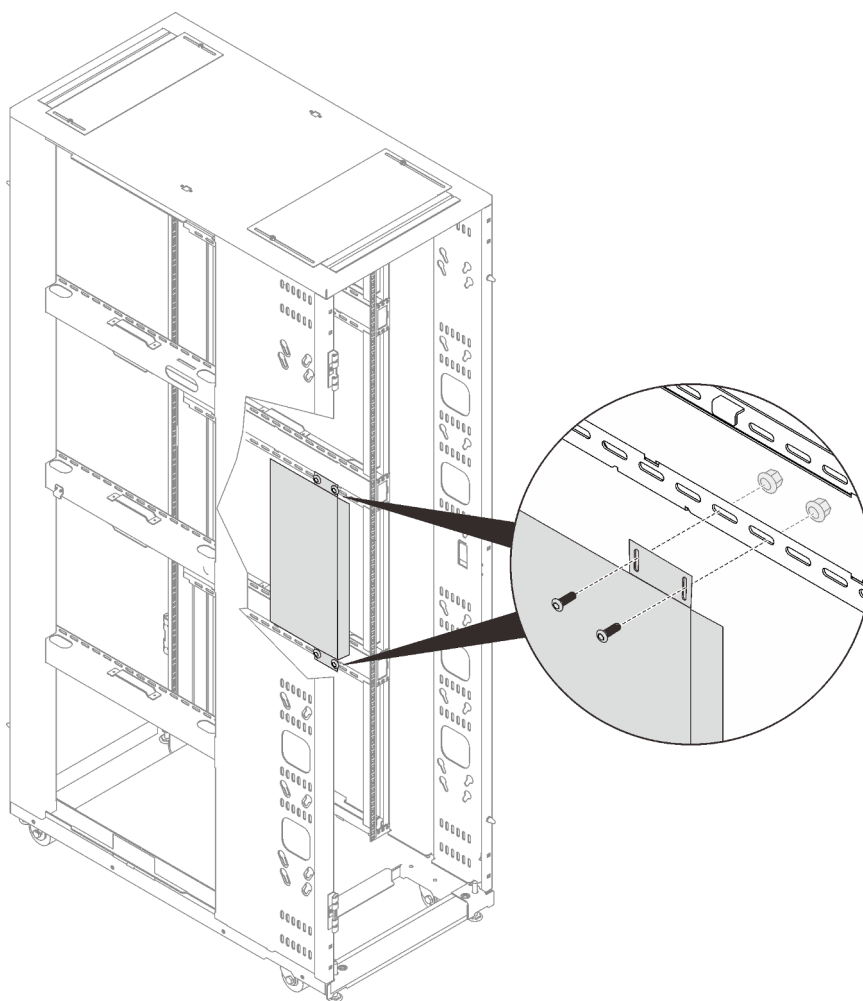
Installazione di un dispositivo 1U nella parte laterale del rack
